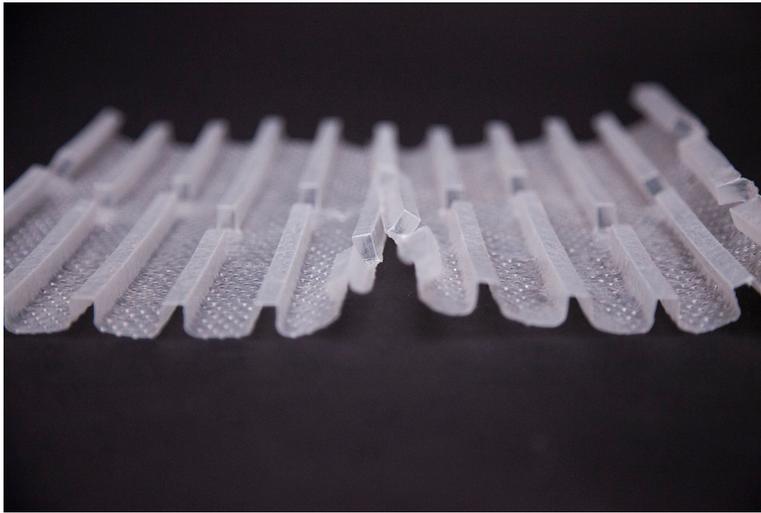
Assemblage par emboîtement de deux modules thermoformés
